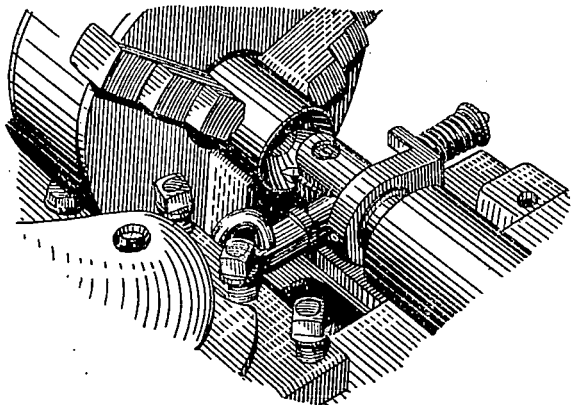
Приспособление для расточки внутренних сферических поверхностей, установленное на станке.
